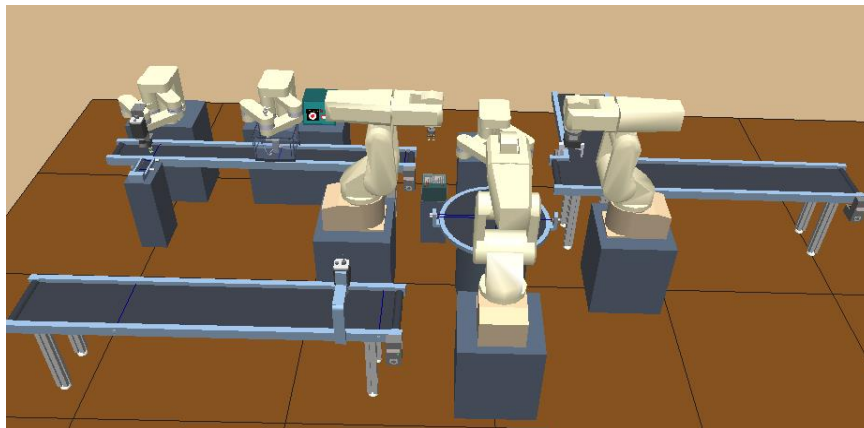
Simulación del sistema del proceso del Ensamblaje y Soldadura de la tarjeta impresa, vista de frente [10]
